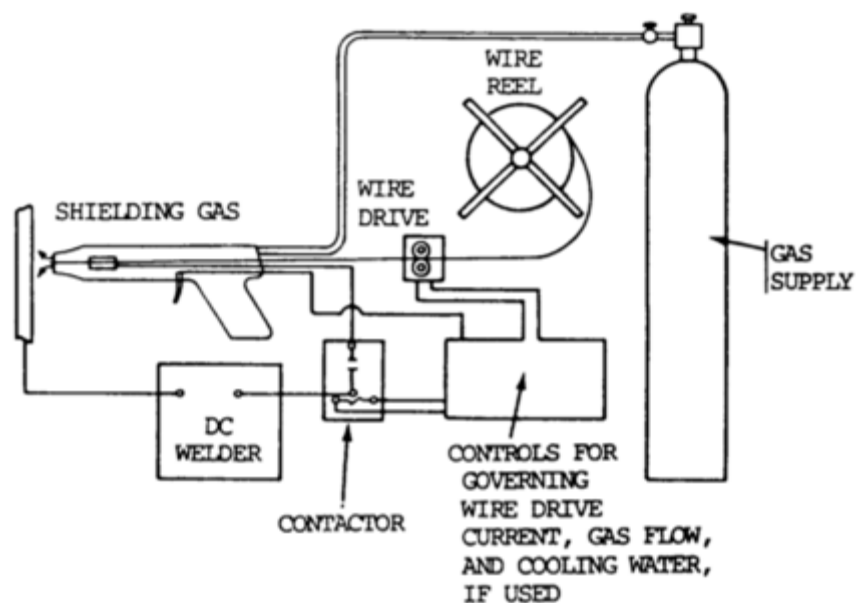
Processo de soldadura MIG [1].
